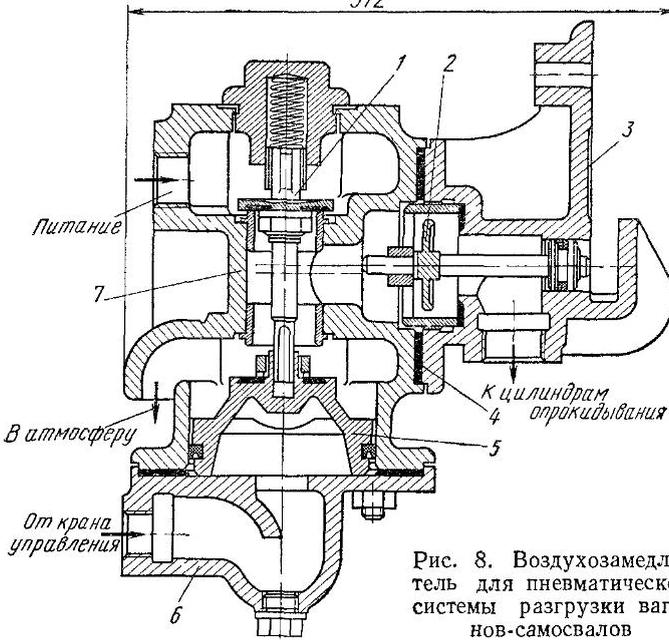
Воздухозамедлитель для пневматической системы разгрузки вагонов-самосвалов
